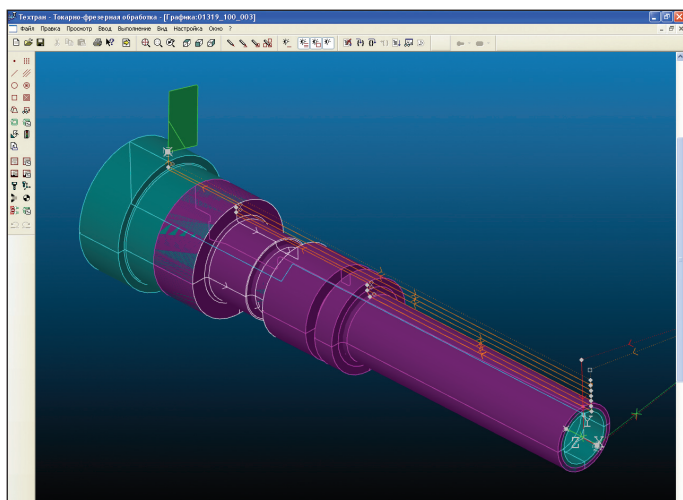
Токарная деталь и заготовка (произвольный вид)
